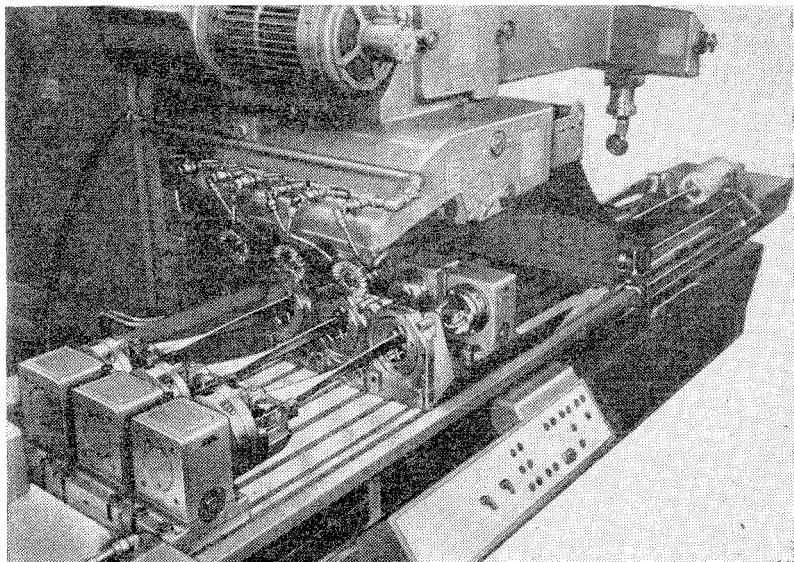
Копировально-фрезерный станок для поперечного кругового фрезерования рабочих частей лопаток большой длины
